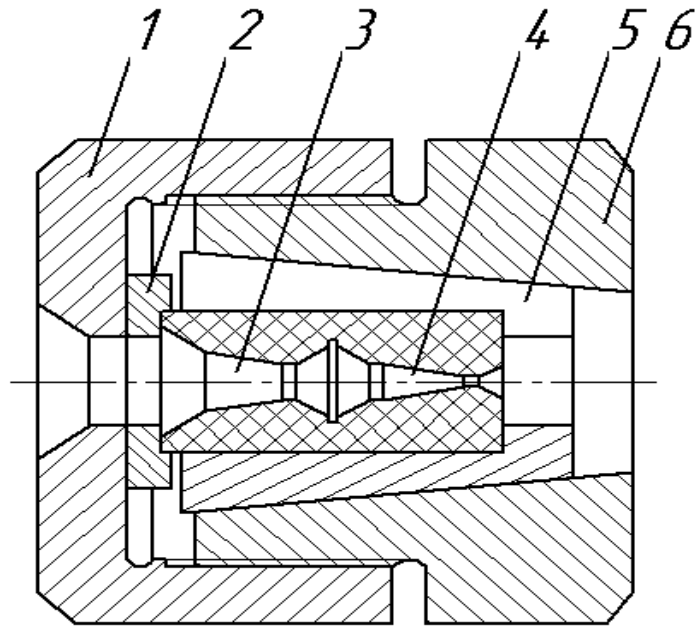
Збірна волока конструкції В.Л. Колмогорова і др.: 1-затискна гайка; 2-шайба; 3-напорна волока; 4-робоча волока; 5-цангова (розрізна) втулка; 6-корпус
